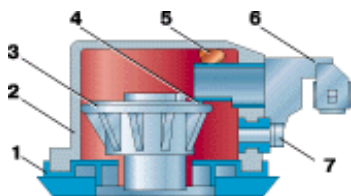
Схема регулировки зазора в датчике порядкового номера цилиндра: 1 – установочная пластина; 2 – корпус; 3 – ротор; 4 – установочный выступ; 5 – пружина; 6 – чувствительный элемент; 7 – винт крепления чувствительного элемента
